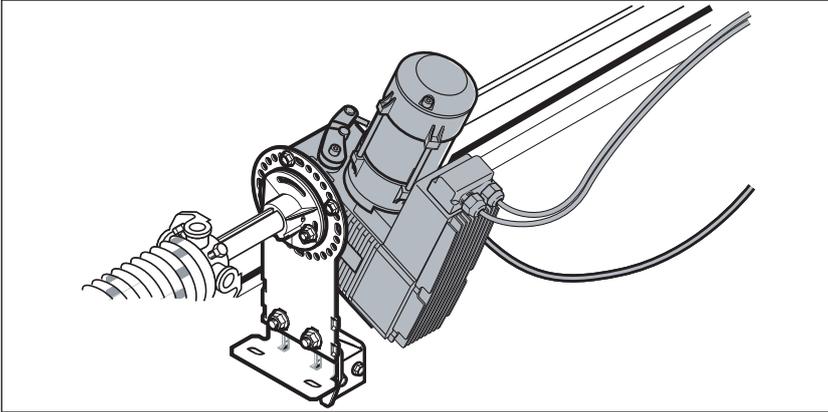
Montageart Tor-Mitte , Beschlag HU/VU
